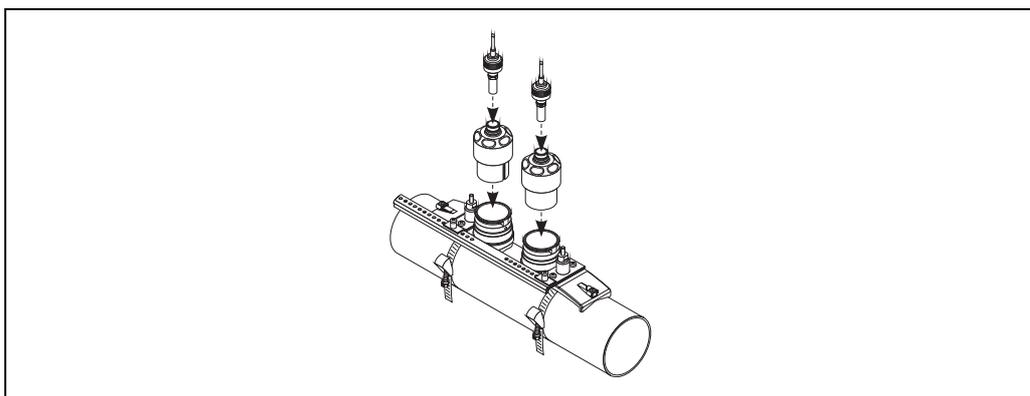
Montaggio del sensore e collegamento del cavo di collegamento
